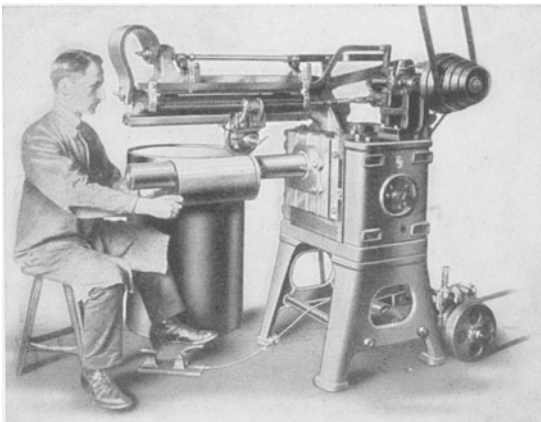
Rollenschnitt-Nahtschweißmaschine mit Wanderrolle.
